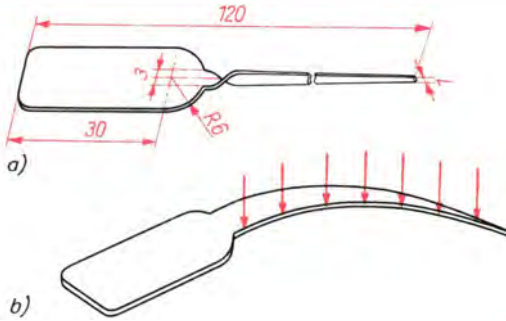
Vom »Türkensäbel« zum Zeiger: a) Maße des Zeigers, b) Richten des Zeigers durch leichte Hammerschläge
